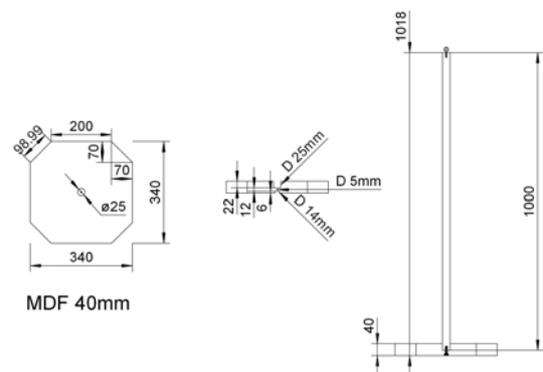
Absperrpoller, verschraubt mit M4 Innensechskant-Schraube mit U-Scheibe
